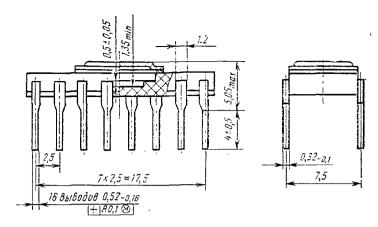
Конструкция металлокерамического корпуса 2103 (201.8-1)
